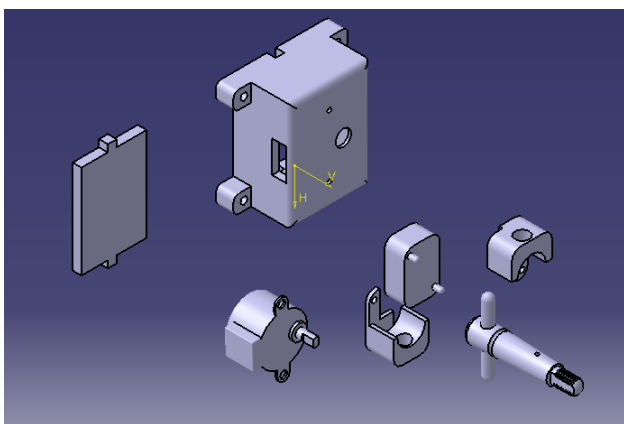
CAD do modo explosão dos adaptadores e a torneira da bureta
